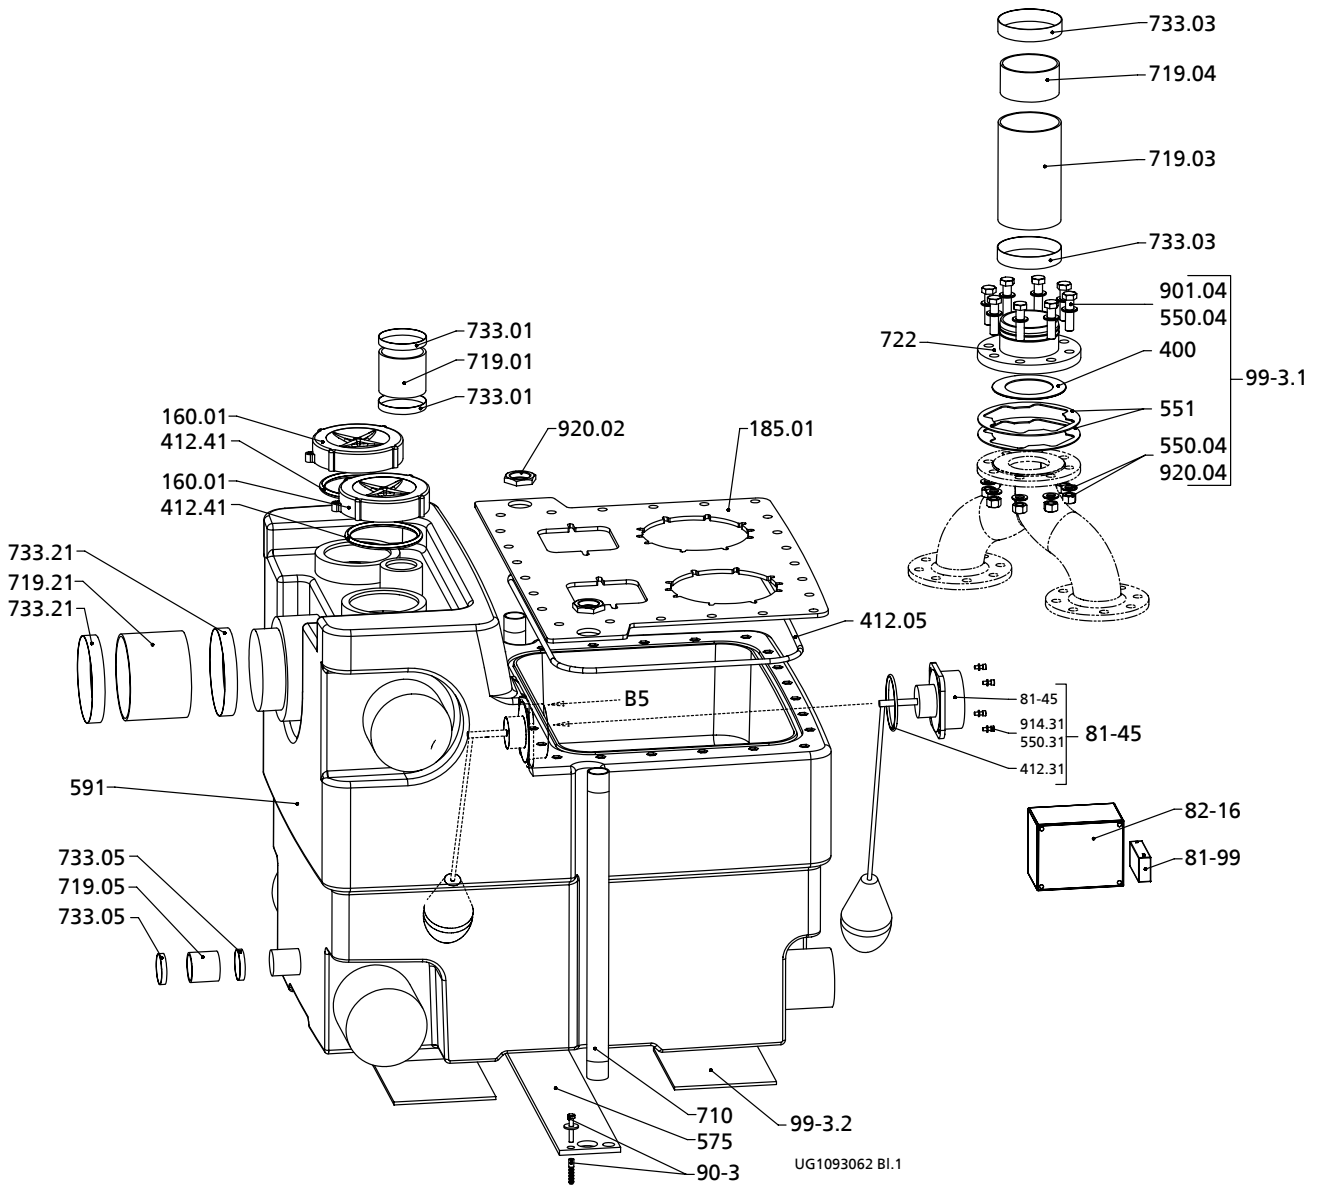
Покомпонентный сборочный чертеж Компакта UZ450 и UZ900
